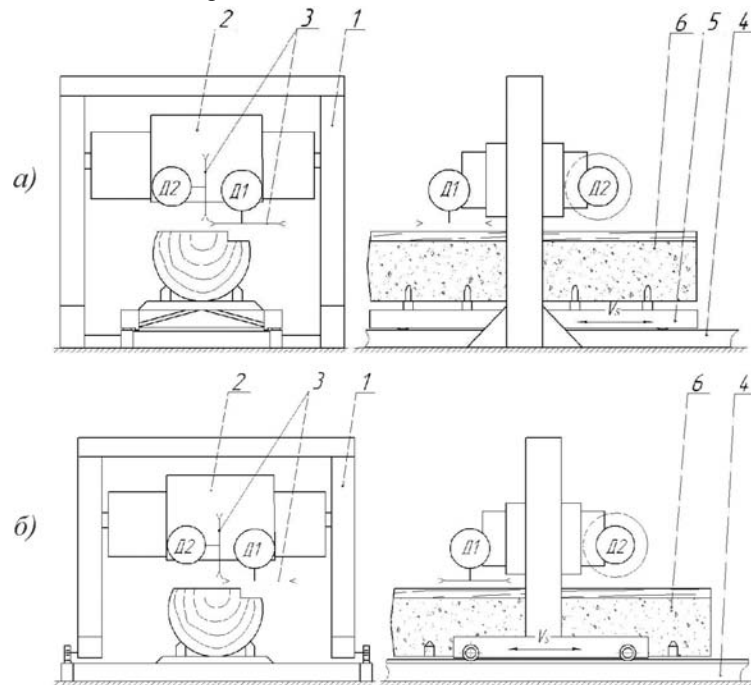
Принципові схеми верстатів ортопилення: а – рух подавання виконується візком із заготовкою; б – рух подавання виконується супортом з інструментом; 1 – каретка; 2 – супорт; 3 – кругла пилка; 4 – станина; 5 – візок; 6 – колода
